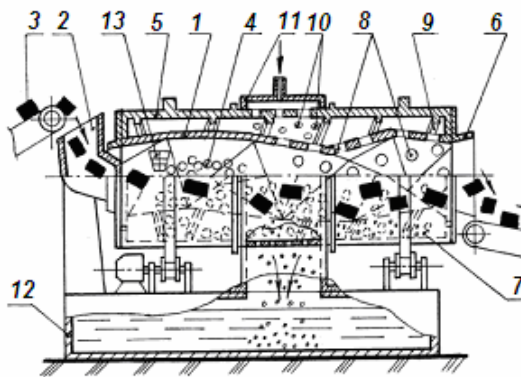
Установка для непрерывной отделочно - зачистной обработки деталей
